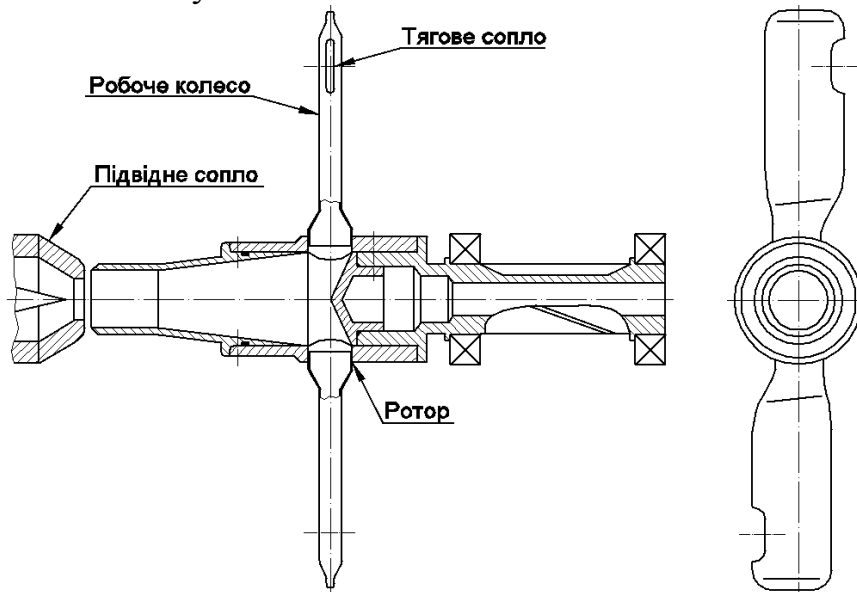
Схема струминно-реактивної розширювальної машини
